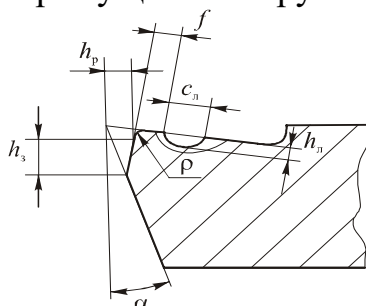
Зоны износа режущего клина в главной секущей плоскости
